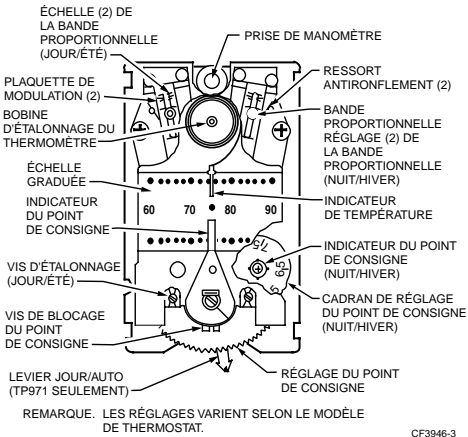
Indicateurs et leviers de réglage des TP971 et TP972A2218, vu du devant sans couvercle.
